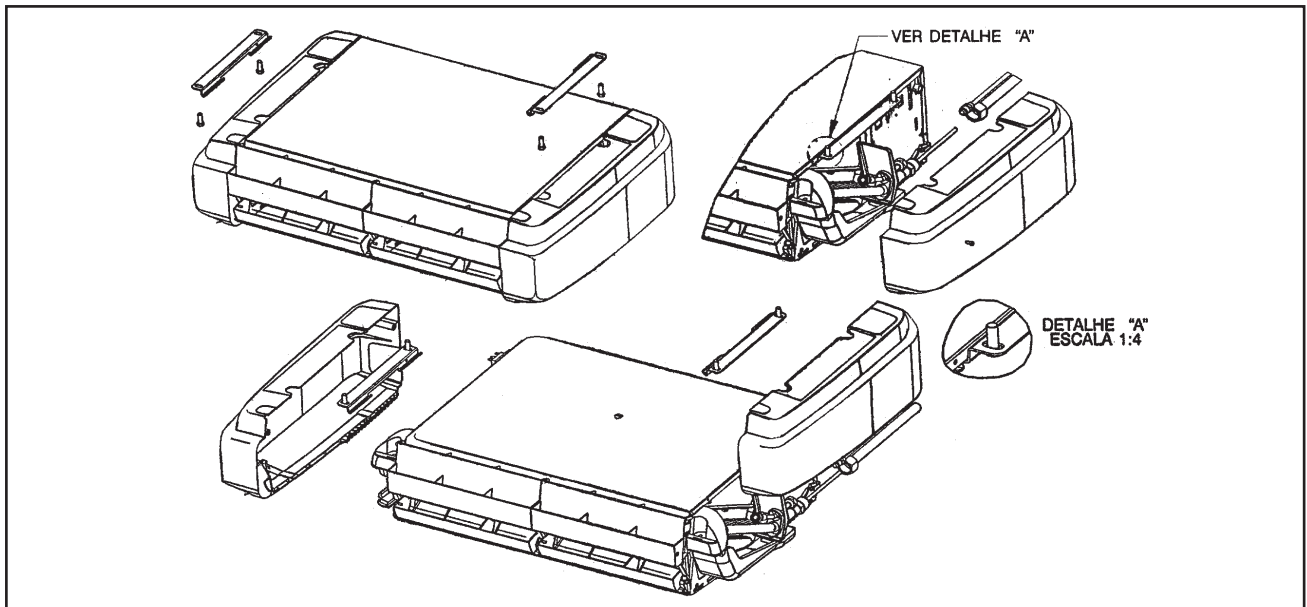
MONTAGEM DO SUPORTE DE FIXAÇÃO
